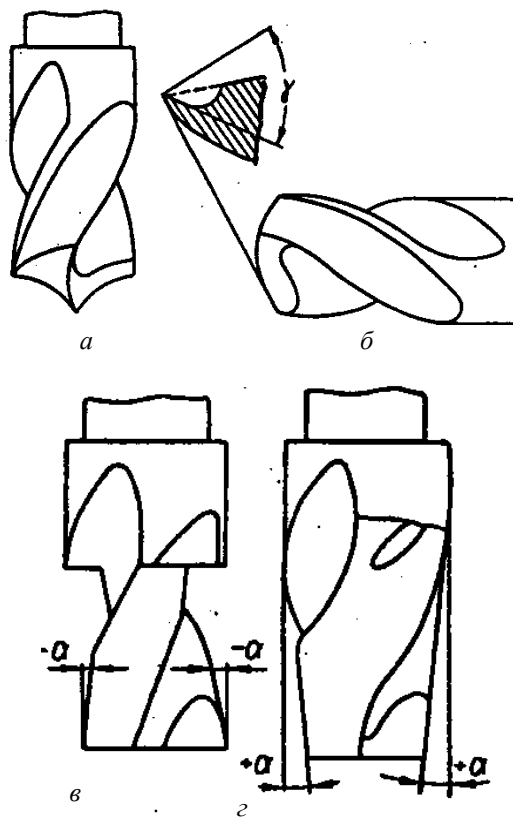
Фрезы, изготовленные из отработанных сверл: а – фреза с вогнутой режущей кромкой; б – с выпуклой режущей кромкой; в, г – конические фрезы
